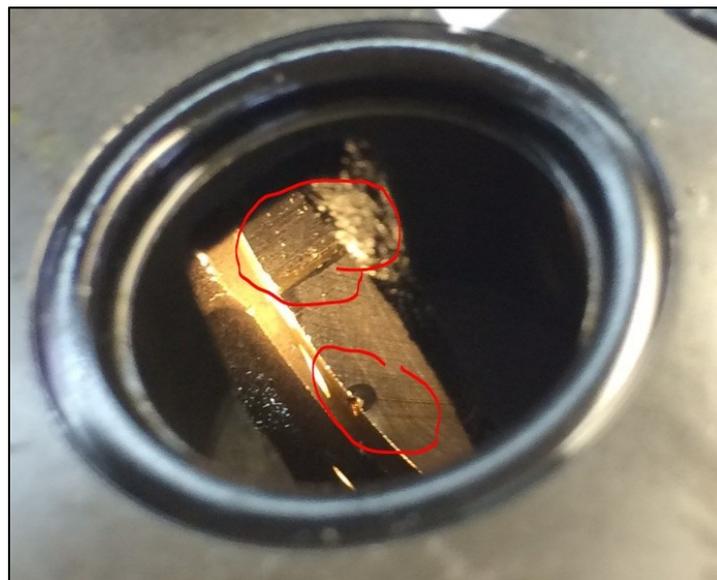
Beschädigungen an der Steuerkante des Kolbens³⁷
